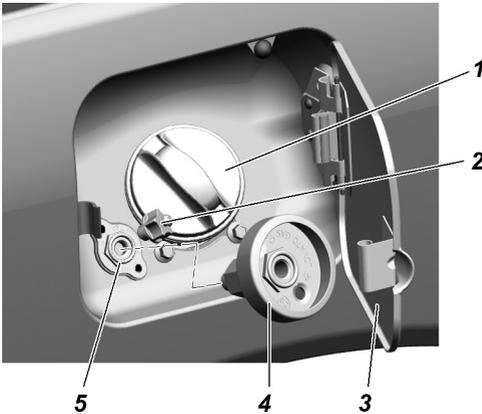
Заправочный люк для автомобилей УАЗ-236321, УАЗ-236322:
